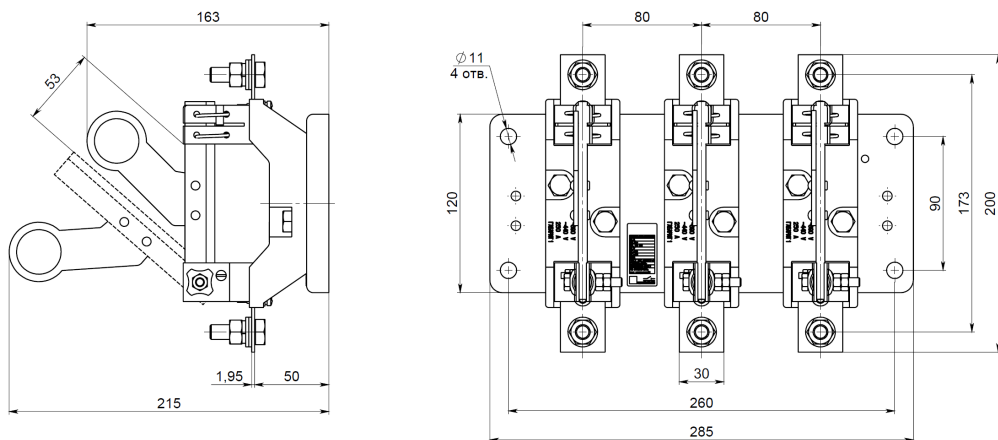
Разъединитель РЕ19-31(35)-31190-00 УХЛЗ с центральным рычагом для управления штангой, масса 3,02 кг
